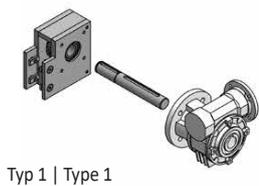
eingebaute Steckwelle | Fig.2: mounted insert shaft
